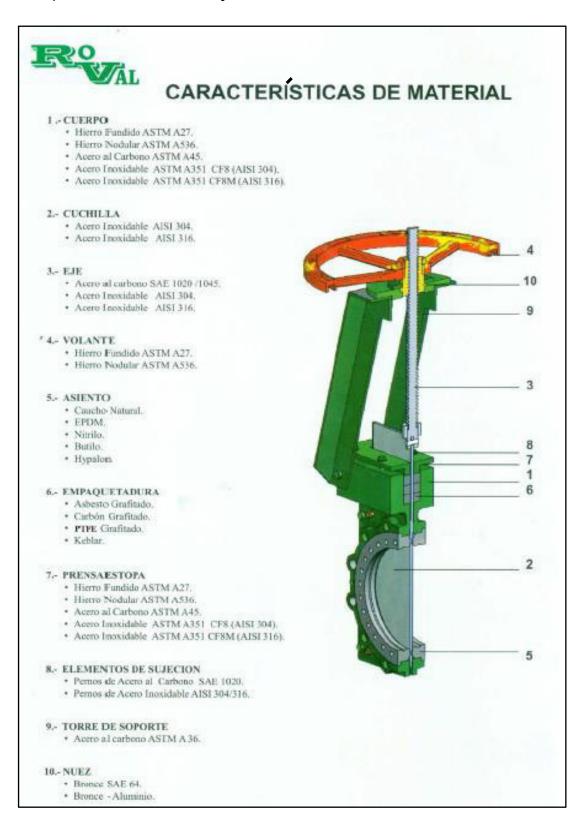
Partes y Características de la Válvula de cuchilla Fuente: La empresa
